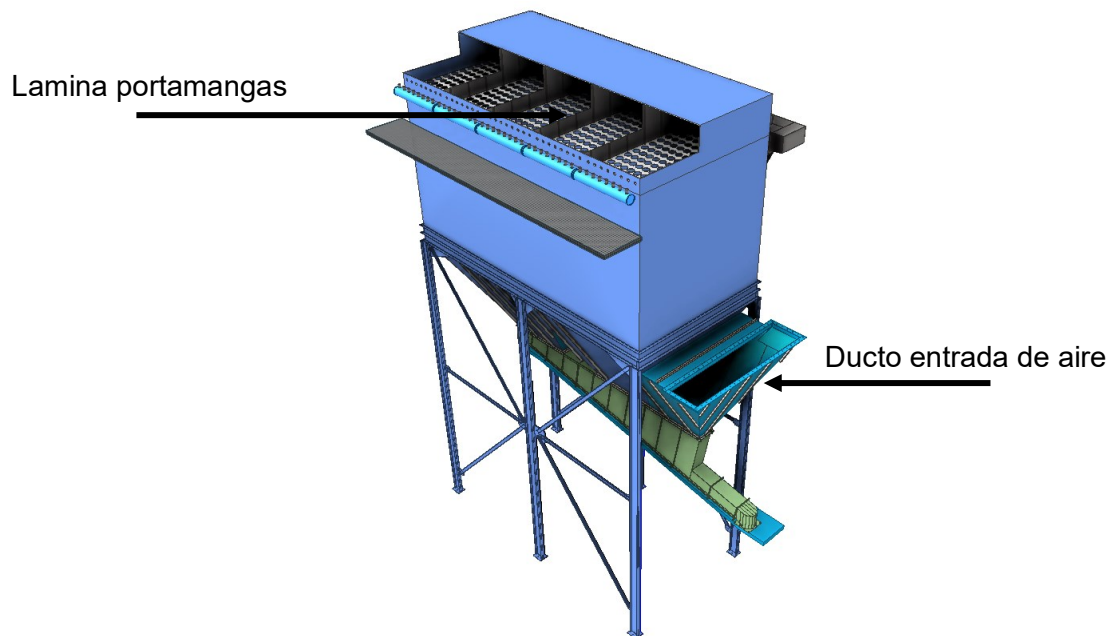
Vista Alzado Filtro de Mangas, Molienda de Crudo.
